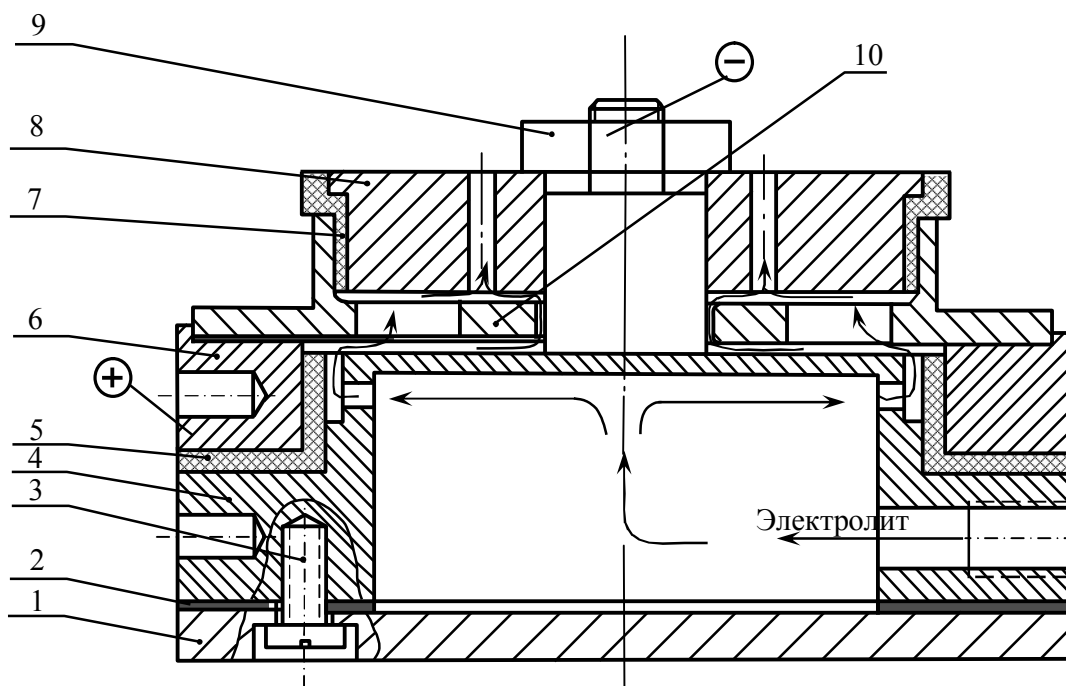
Схема приспособления для двухстороннего скругления острых кромок элементов фрикционного диска с утопленным фланцем:
